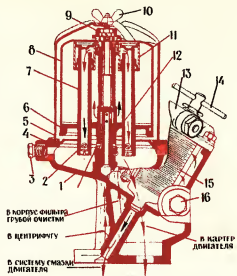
Масляные фильтры двигателя ЗИЛ-130: 1 — корпус масляных фильтров; 2 — иннерлер центробежного фильтра тонкой очистки (центрифуга); 3 — пробка; 4 — прокладочная конусная; 5 — конус; 6 — уплотнительное кольцо; 7 — корпус фильтра тонкой очистки; 8 — крышка корпуса; 9 — гайка; 10 — гайка-барашек; 11 — сетчатый фильтр; 12 — ось; 13 — крышка фильтра грубой очистки; 14 — рукоятка; 15 — фильтр грубой очистки; 16 — пробка для слива масла из фильтра грубой очистки.
